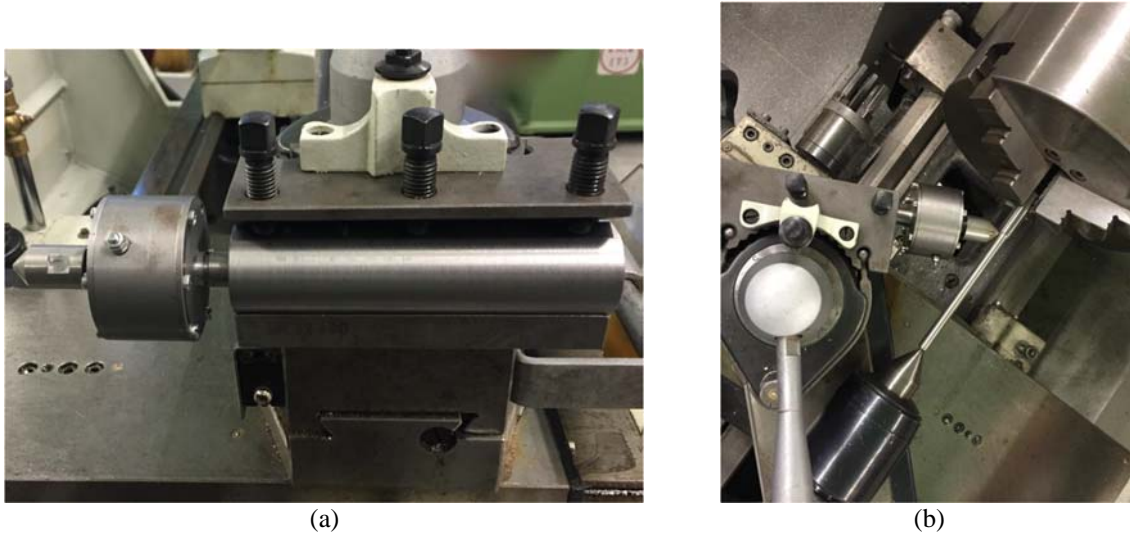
Ensamblaje del conjunto herramienta y portaherramienta en el torno. (a) Vista general. (b) Vista superior donde se puede ver el proceso de bruñido del radio de acuerdo de las probetas.
